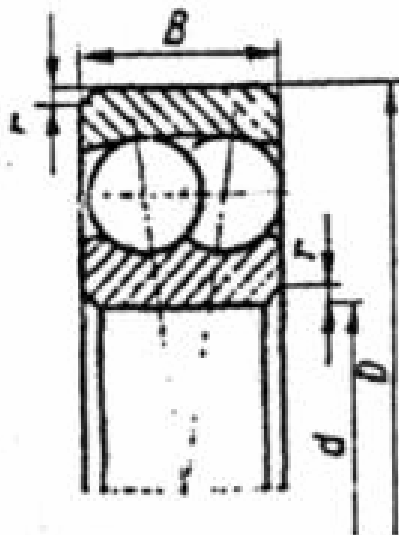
Підшипник кульковий радіальний сферичний дворядний (ГОСТ 28428-90)
